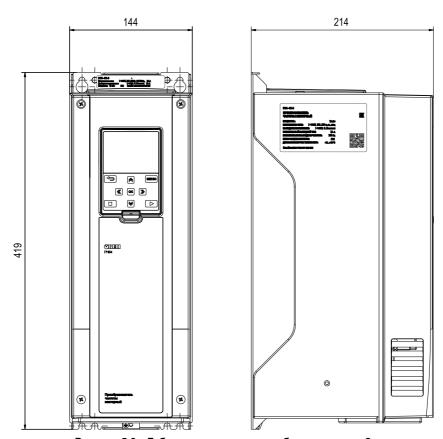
Габаритные размеры прибора в корпусе 2
